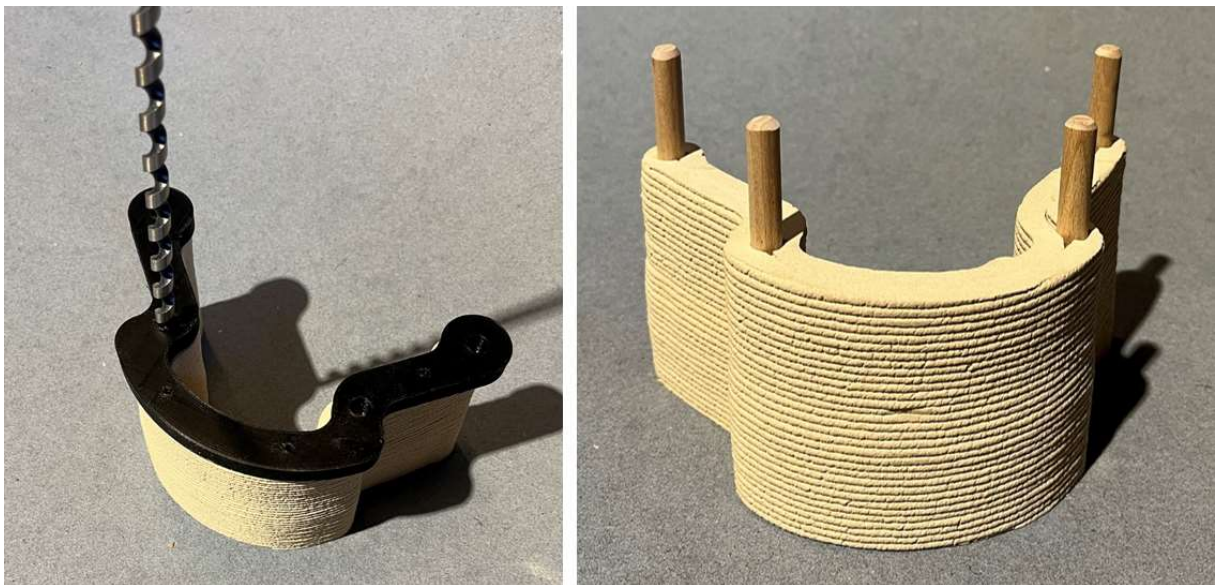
Aufbohren mit Bohrschablone und Schlangenbohrer (links), Dübel in der Möbelecke befestigt (rechts)
